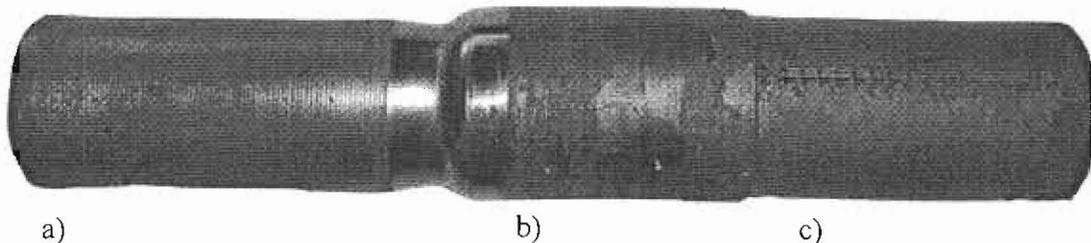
Bohrungsdrücktes Halbzeug bei 680-700°C: a) Hohlteil, b) ursprüngliches Halbzeug, c) Probenträger
